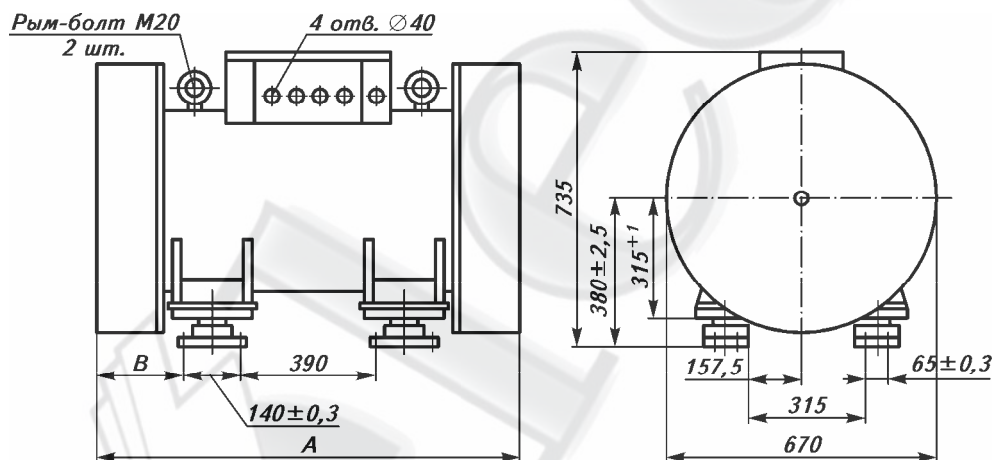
Общий вид, габаритные и установочные размеры агрегатов АГПМ
